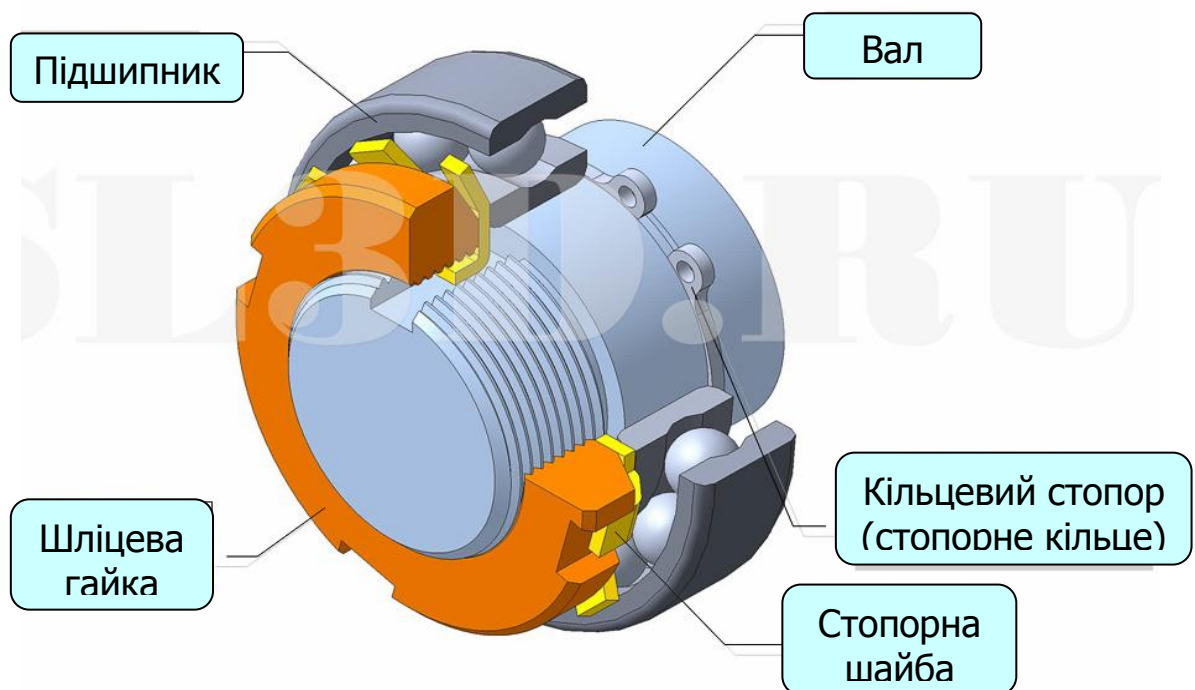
Установка підшипника з упором в кільцевий стопор
